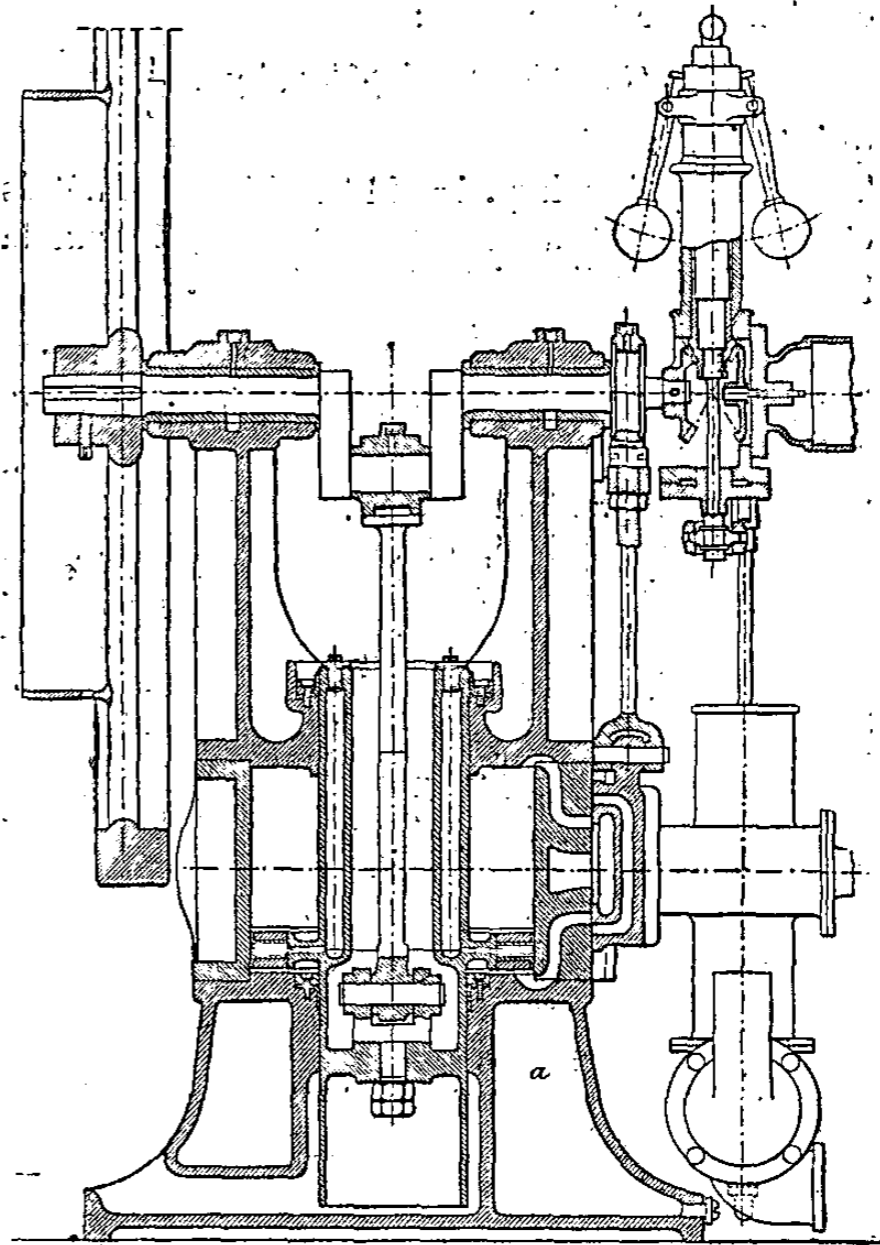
Moteur à fourreau mû par l'air raréfié. Elevation, coupe verticale.
